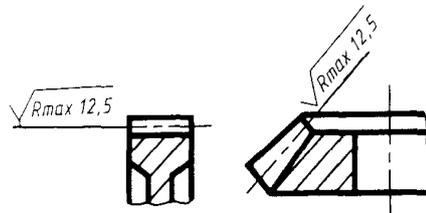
Обозначение шероховатости на зубчатых поверхностях
